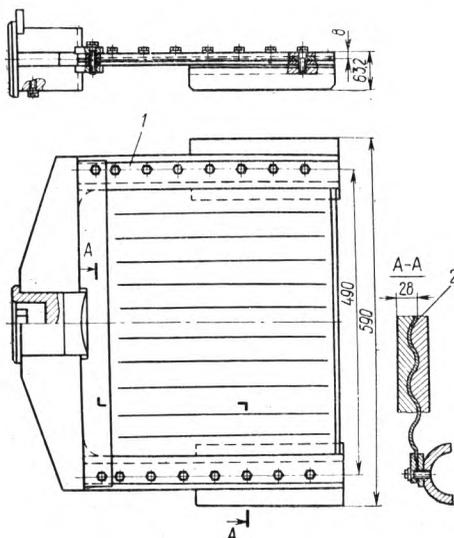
Волнистый нож с прямолинейными волнами: 1 — ножедержатель; 2 — нож
